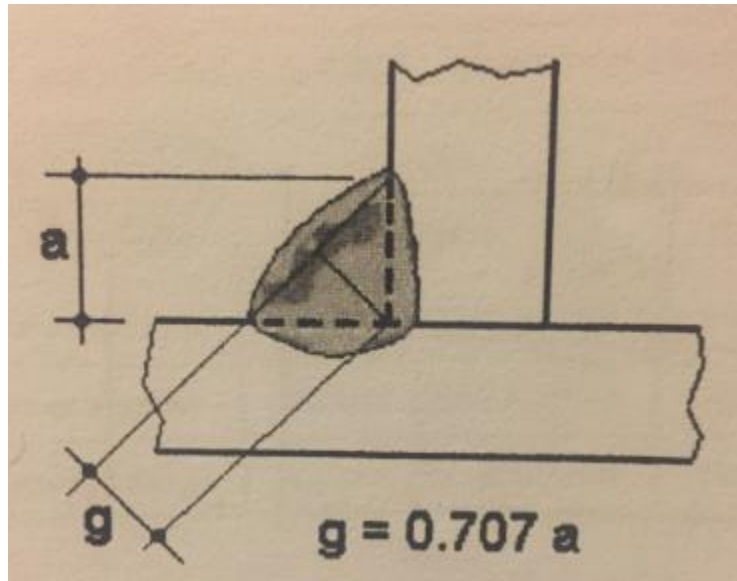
Área efectiva de soldadura de Filete.
